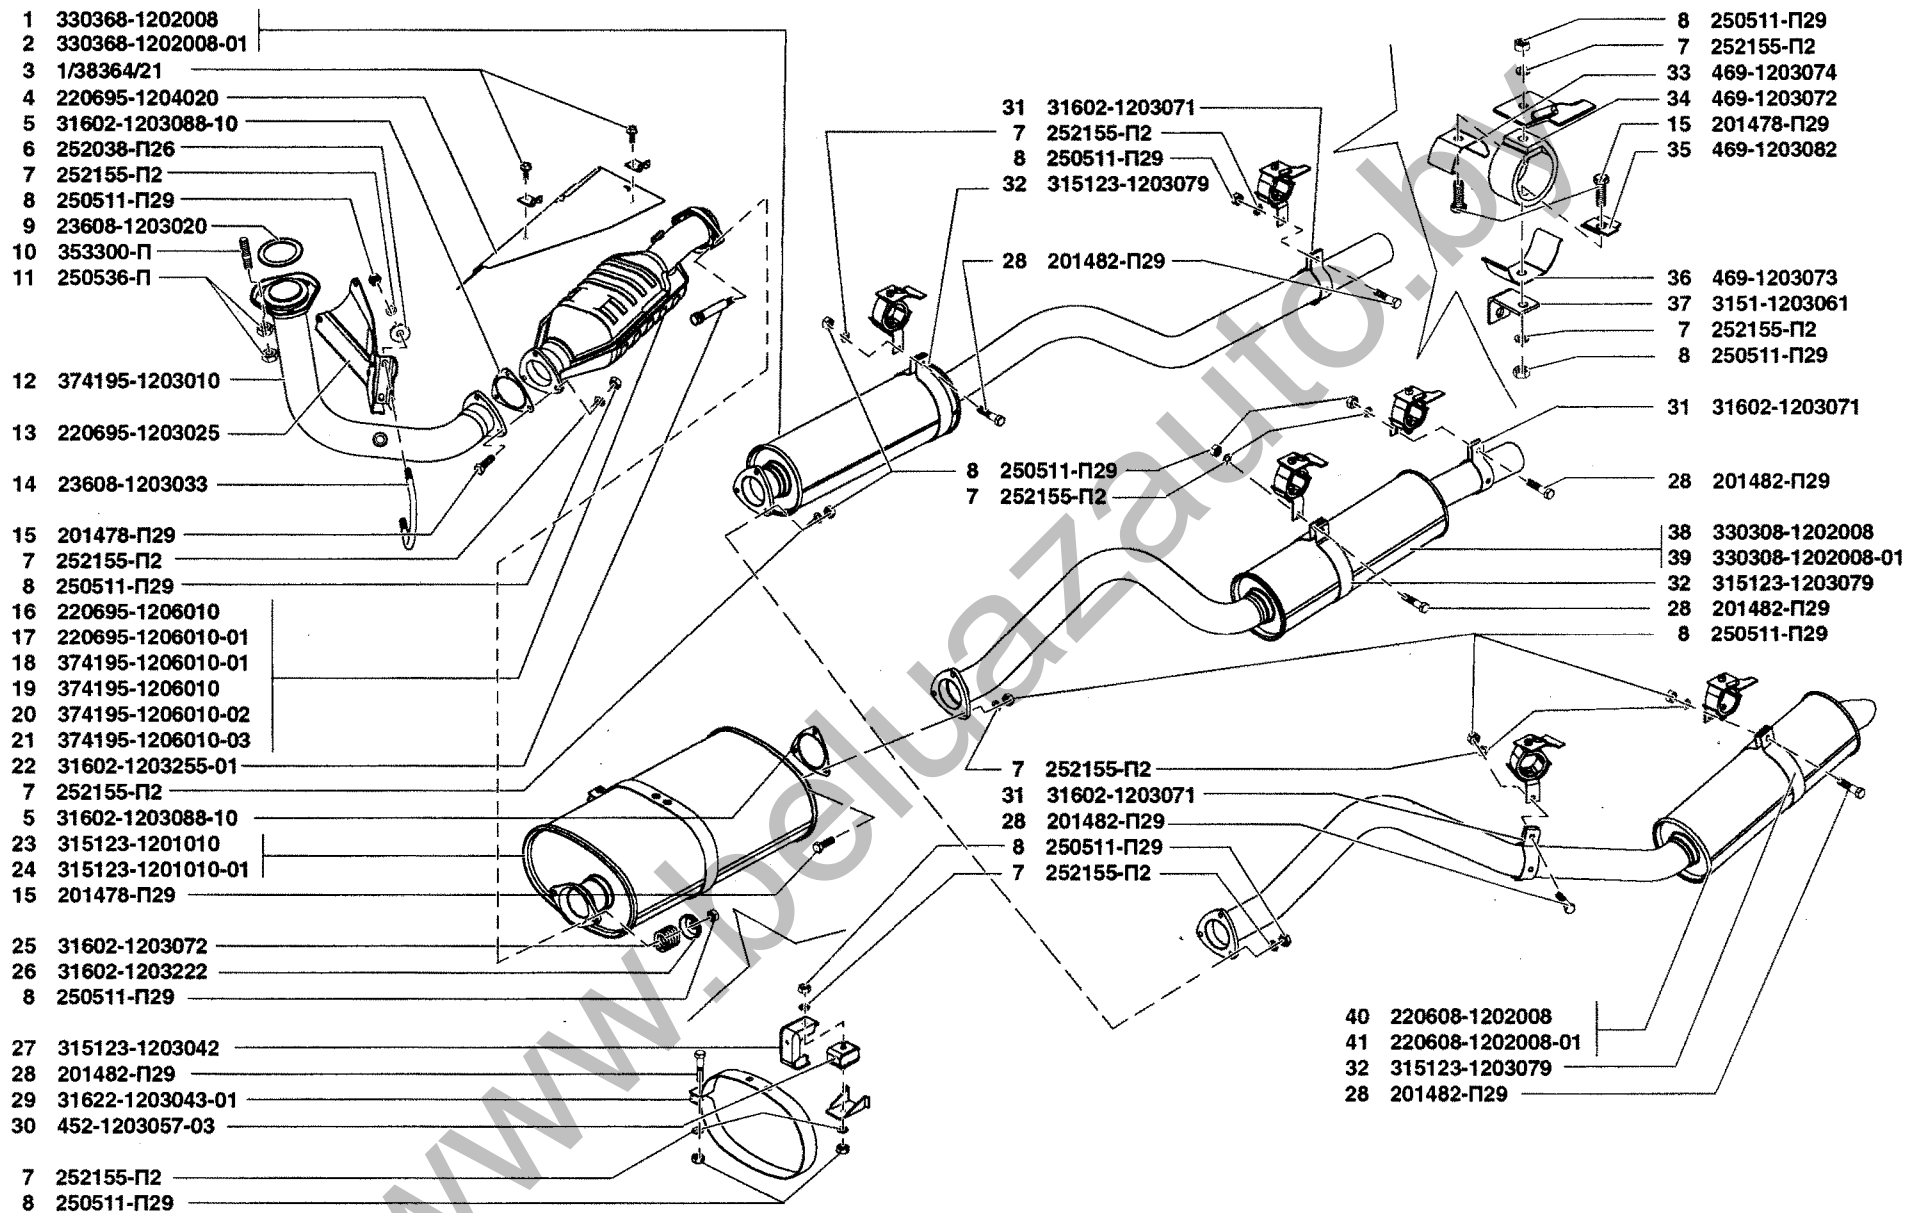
Глушитель выхлопа (1201), резонатор (1202), трубы и подвеска глушителя выхлопа (1203), ограждение глушителя и выхлопных труб (1204), нейтрализатор выхлопных газов (1206)
